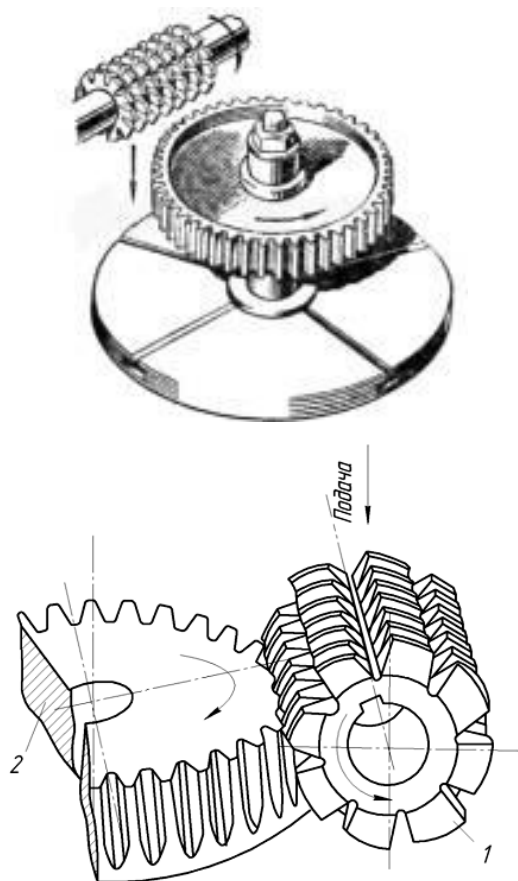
Фрезерування профільних поверхонь методом обкатування черв'ячною фрезою
